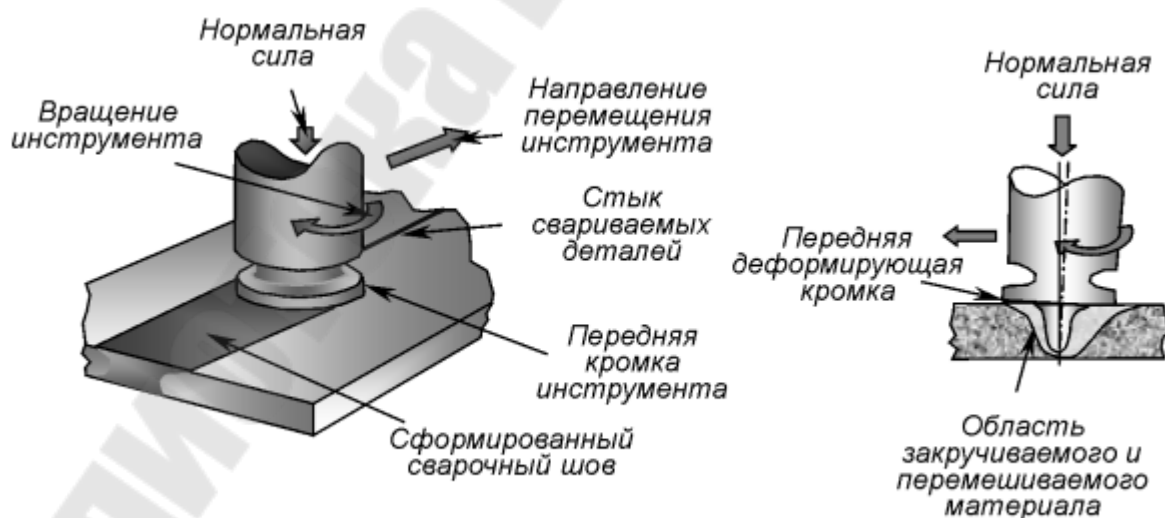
Схема проведения сварки трением полимерных пластин
